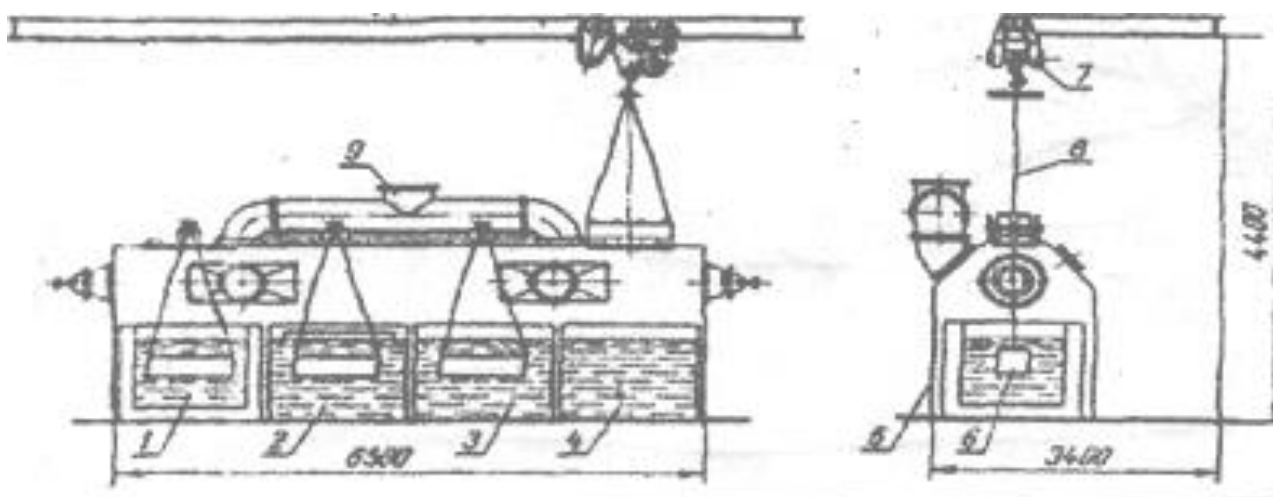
Схема установки ОМ -4265 для очистки нагара и накипи деталей в расплаве солей.
